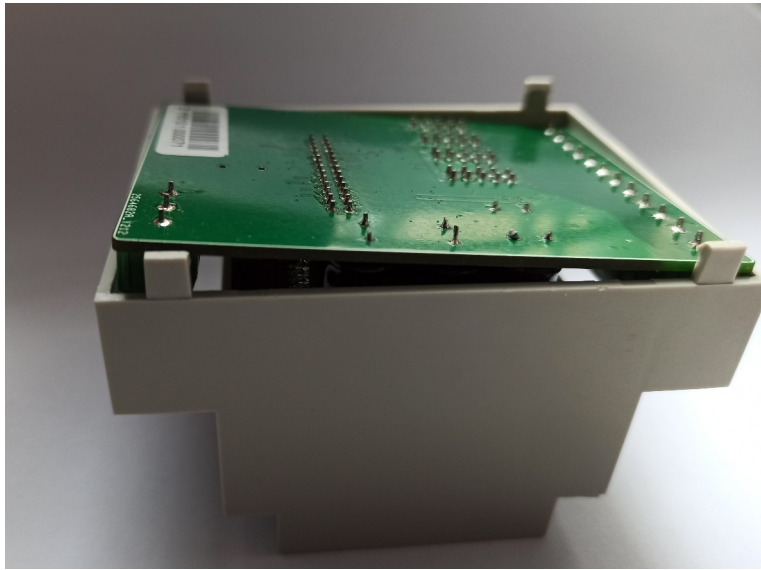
Встановлення плати BASE в корпус (вид знизу)
